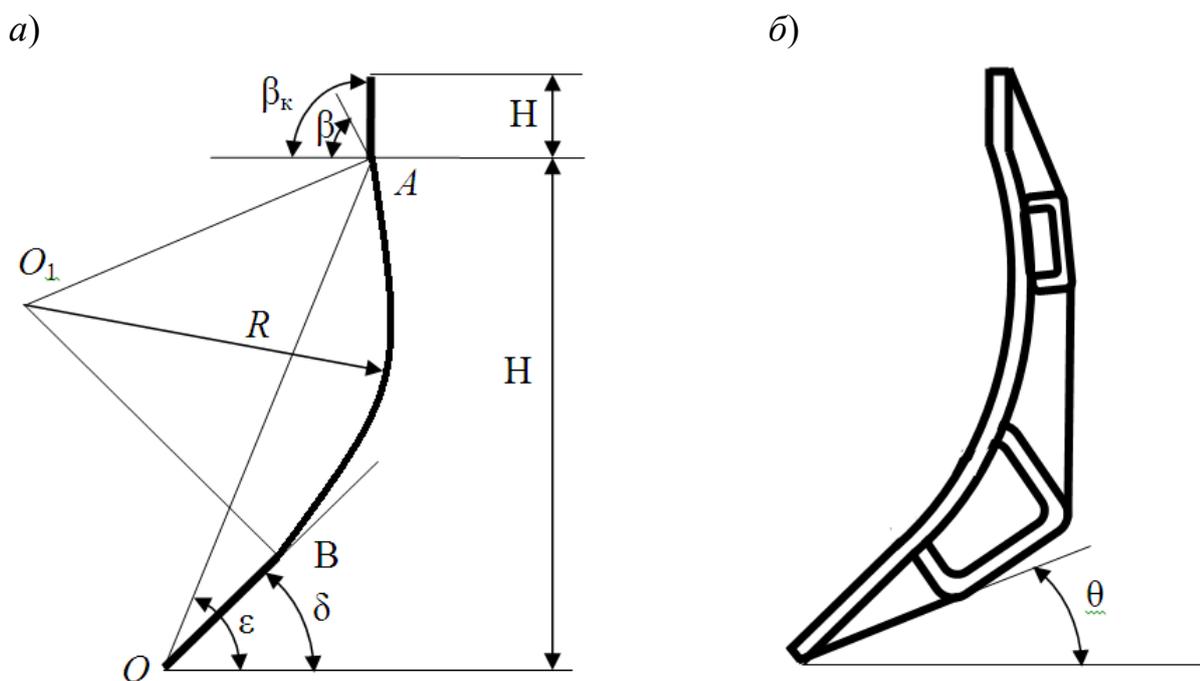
Поперечный профиль (а) и его усиление коробчатыми конструкциями и ребрами жесткости (б)
